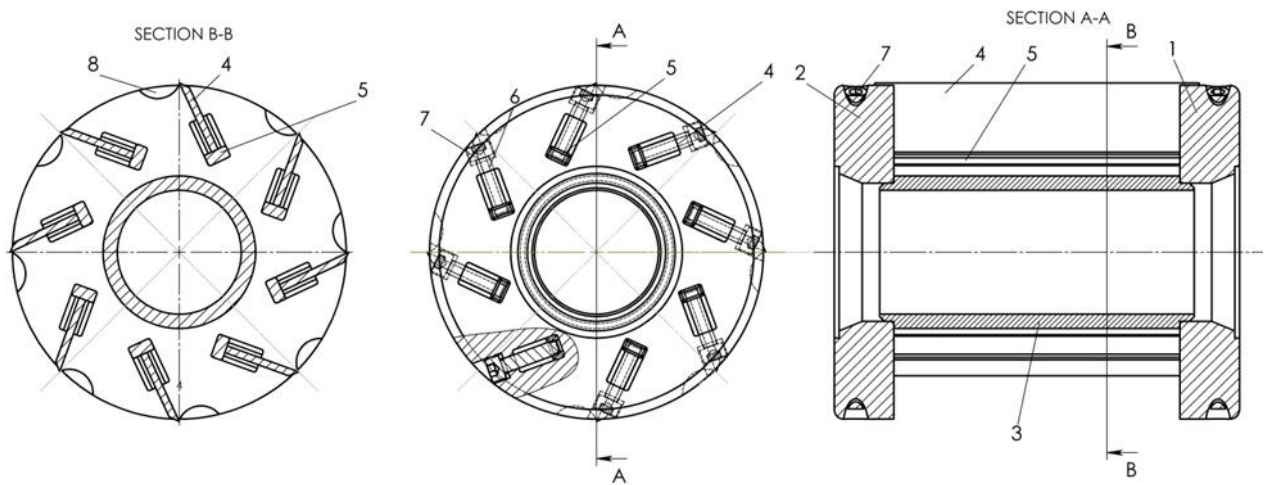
Нова конструкція безкорпусної фрези з самовстановними ножами: 1, 2 – фланці; 3 – втулка; 4 – ніж; 5 – підпірна планка; 6 – прорізь для ножа; 7 – болт; 8 – півкруглий паз для розміщення стружки
